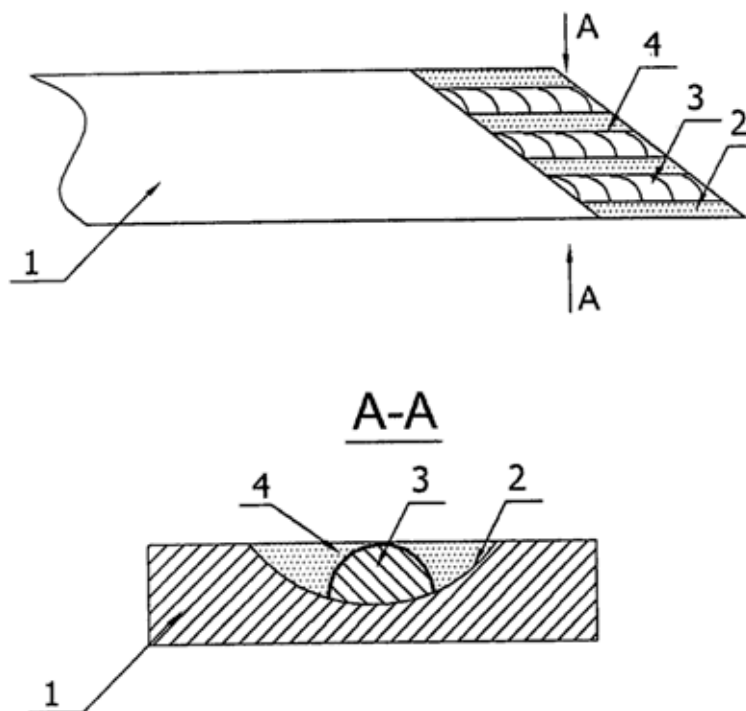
Восстановленный лемех плужного корпуса (1 - рабочая поверхность лемеха, 2 - изношенный участок (лучевидный износ), 3 - наплавленные валики, 4 - песчано-клеевой состав.
